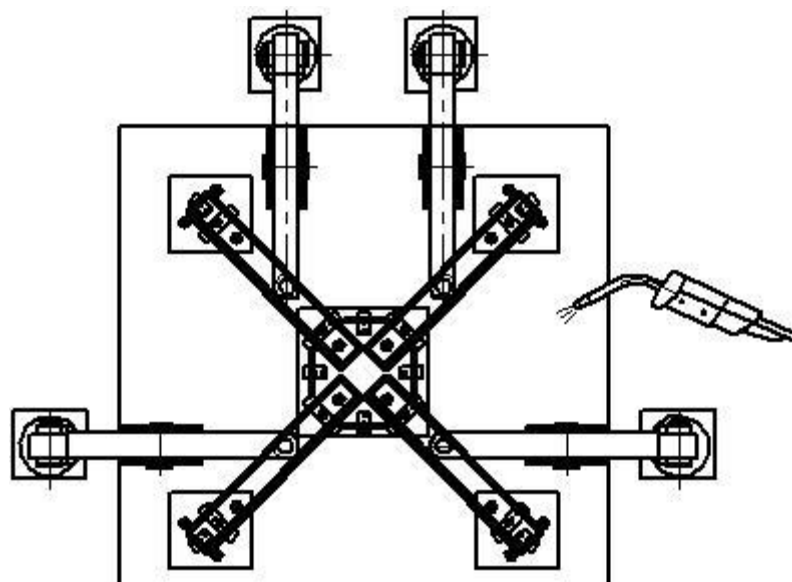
Сборки и сварка раскосой решётки с применением приспособления
